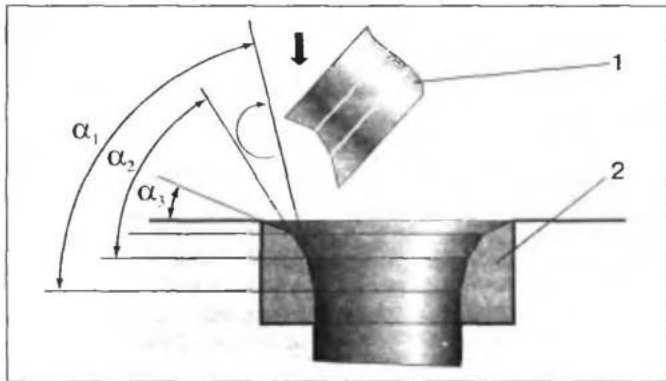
Схема работы комбинированного резца резцовой головки: 1 — резец; 2 — седло
